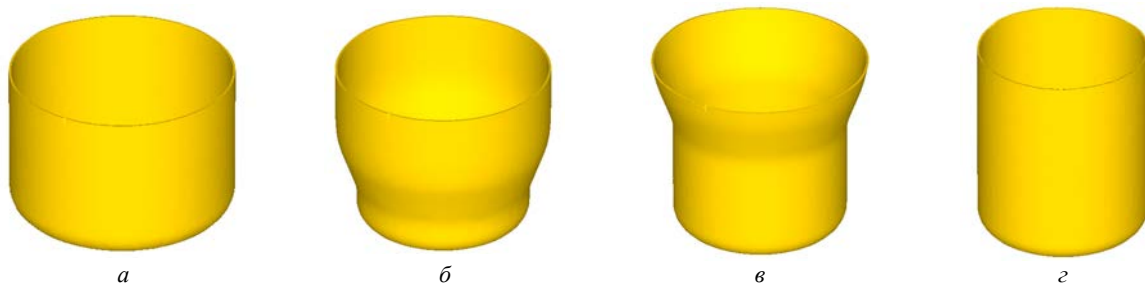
Заготовка на різних етапах другої витяжки без притискання заготовки: а – заготовка, б, в – проміжні стадії витяжки, г – готовий напівфабрикат
